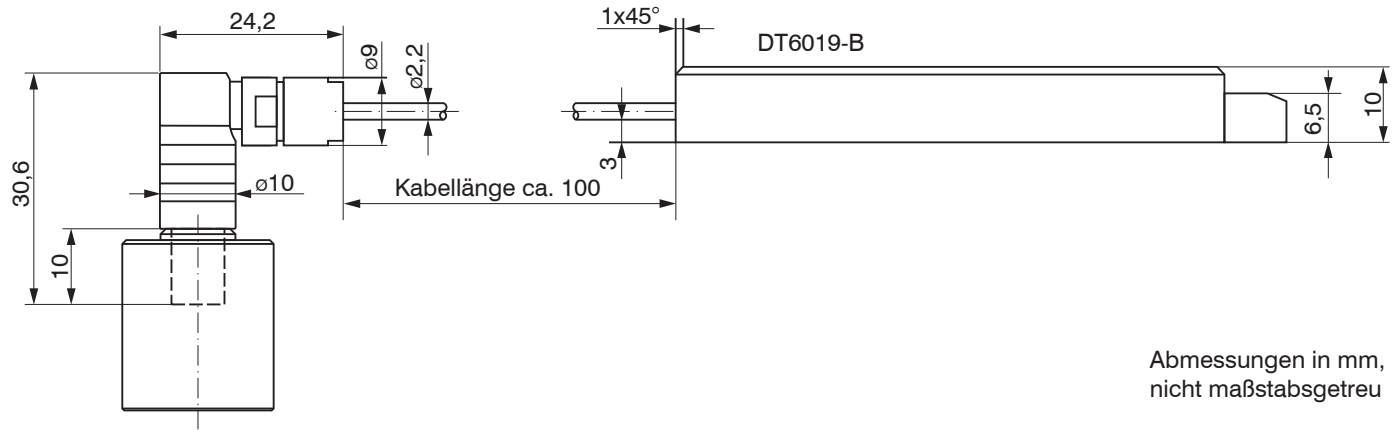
Maßzeichnung Sensorkabel mit Winkel-Stecker für die Sensoren CS02 und CS05
